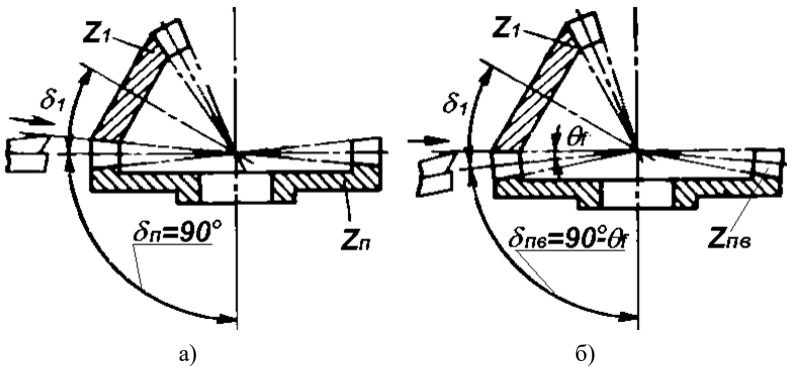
Схеми зачеплення заготовки з твірними колесами: а – плоским; б - плосковершинним
